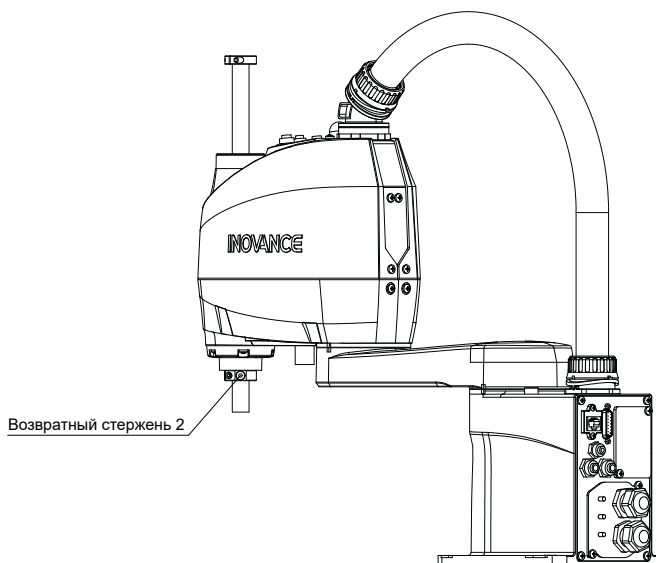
Установка возвратного стержня 2 на ограничительный упор
